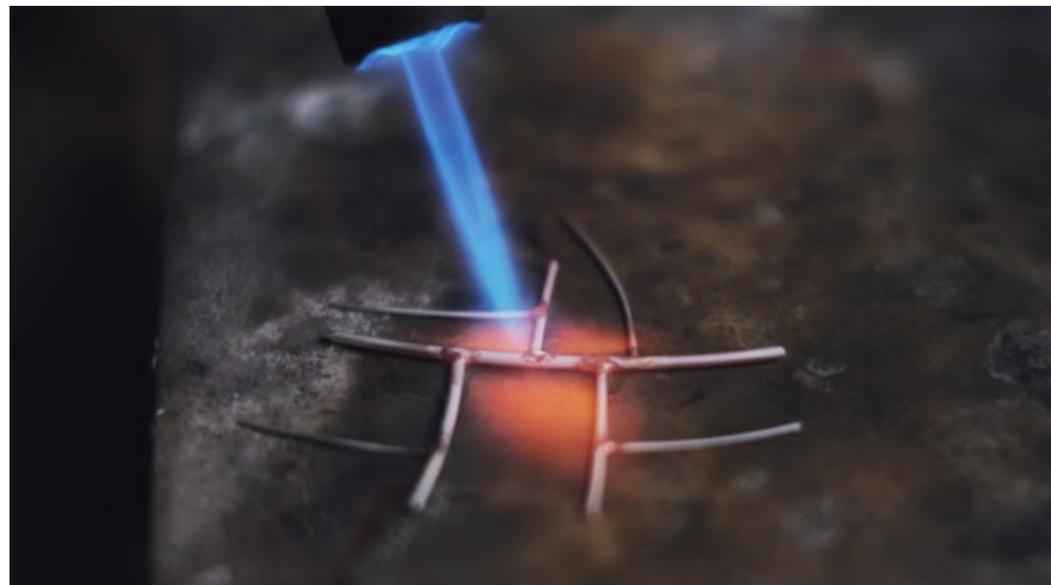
Proceso de soldadura joya-liquen Protousnea. Elaboración propia.
